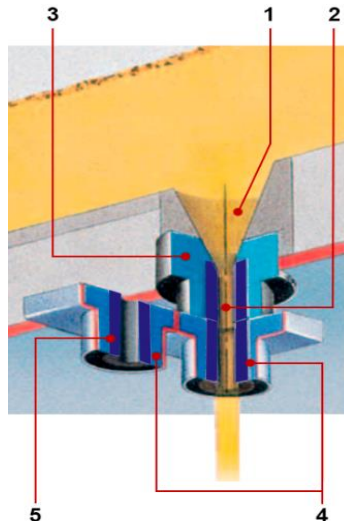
Принципова схема швидкої заміни стакана-дозаторів проміжного ківша сортової МБЛЗ: 1 – лійка набивної маси або формований гніздовий блок; 2 - калібрований струмінь металу; 3- верхній стакан-дозатор типової конструкції; 4 – нижній (змінний) стакан-дозатор; 5 – калібрована ZrO_2 - вставка стакана-дозатора.
